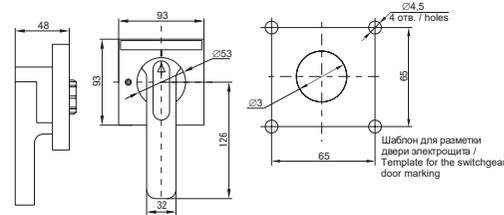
Габаритные размеры устройства, установленного на MCCB / Figure 2 – Overall dimensions of the device mounted on MCCB
